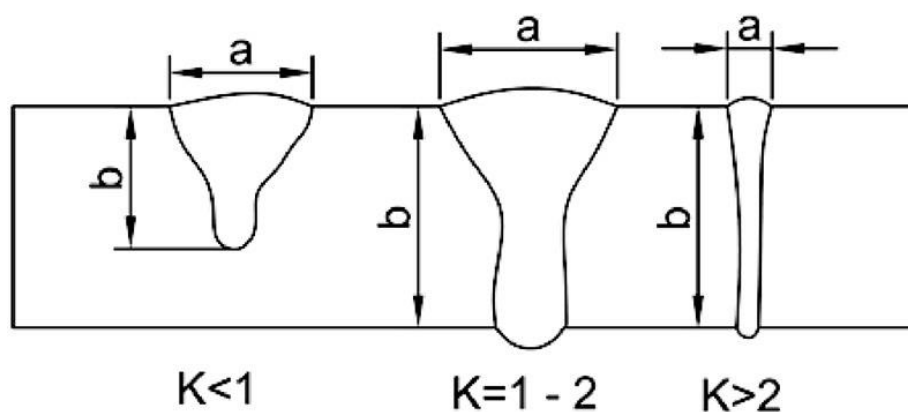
Виды сварных соединений, выполненных методом лазерной сварки
